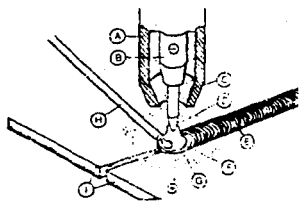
Soldadura con gas inerte TIG. A) Conducción de gas. B) Soporte del electrodo. C) Electrodo de wolframio no consumible. D) Gas de protección. E) Cordón de soldadura. F) Metal fundido. G) Arco. H) Metal de aportación. I) Metal base.
